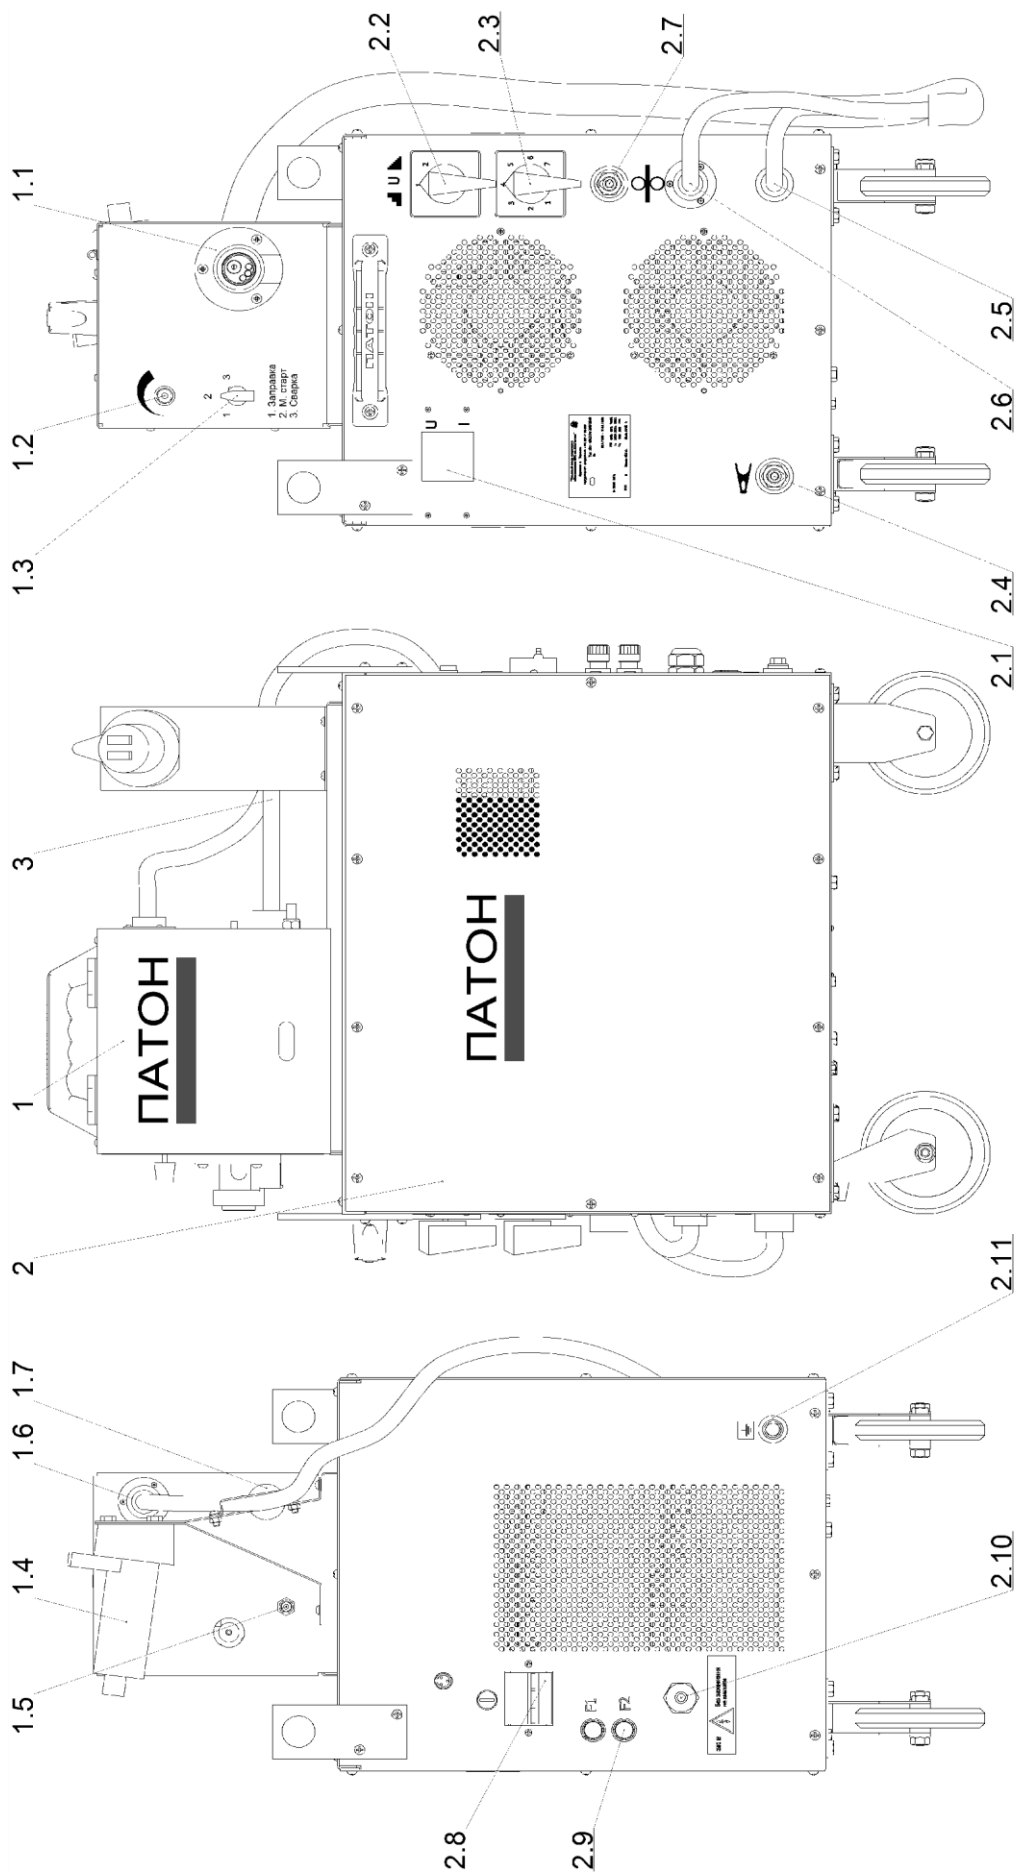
Полуавтомат сварочный и его основные блоки.
